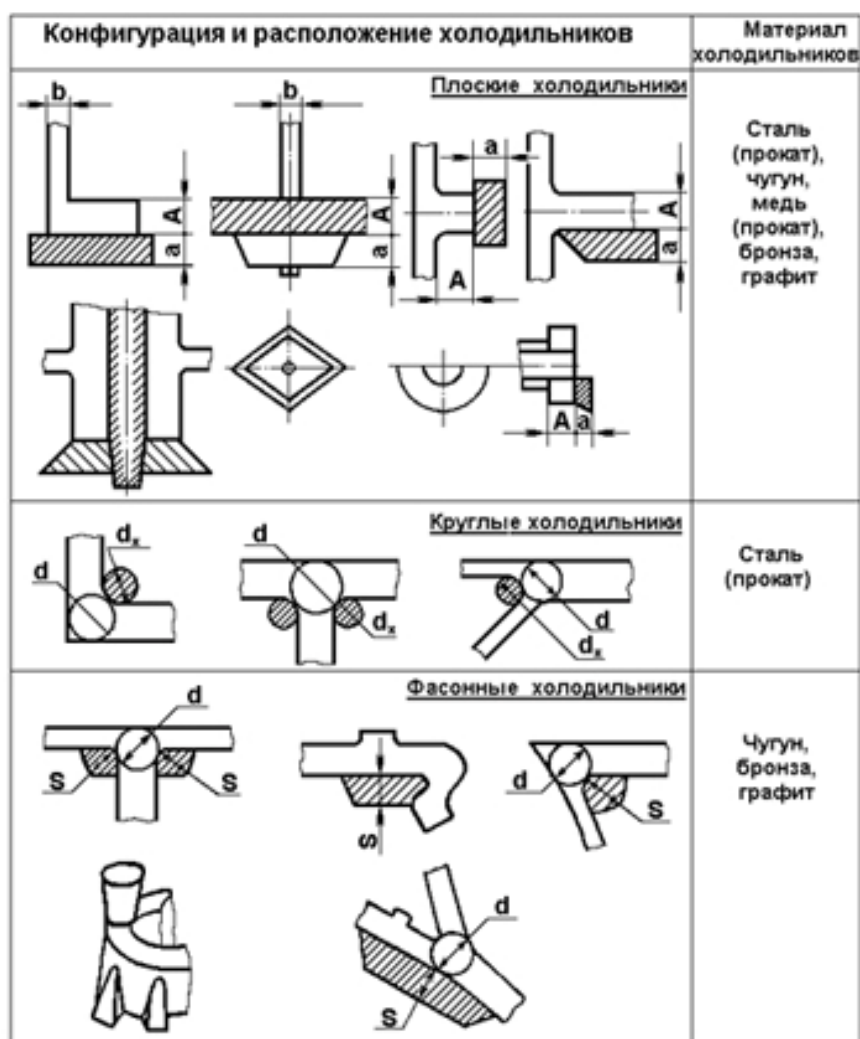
Схемы расположения плоских, круглых и фасонных наружных холодильников
